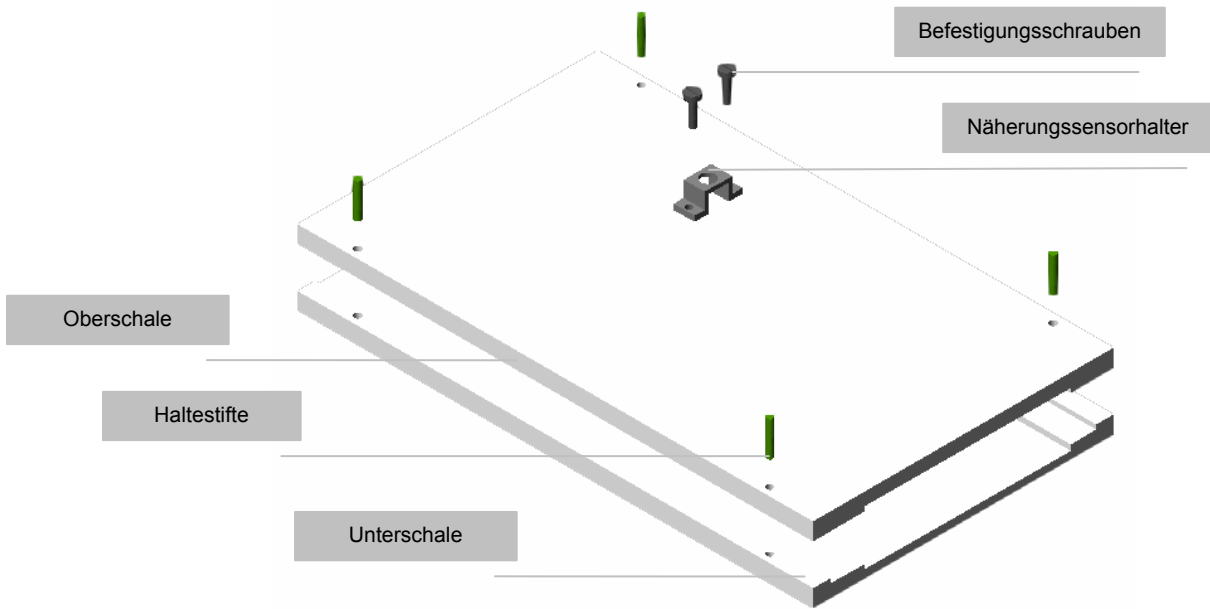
Heizwendelmagazin in Explosionsansicht
